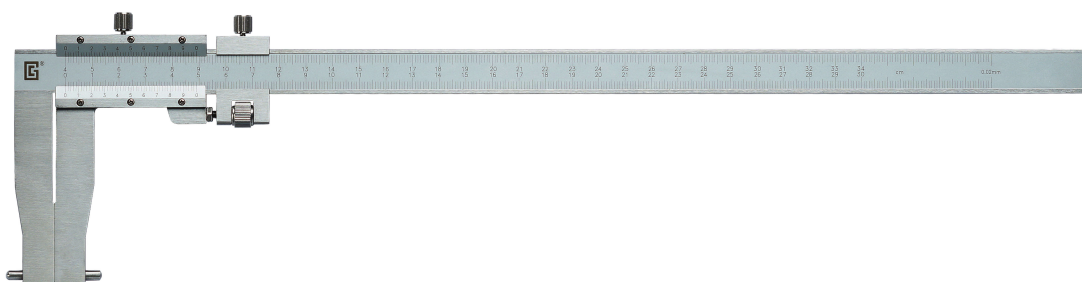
Общий вид штангенциркулей модели ШЦС-115, тип В
